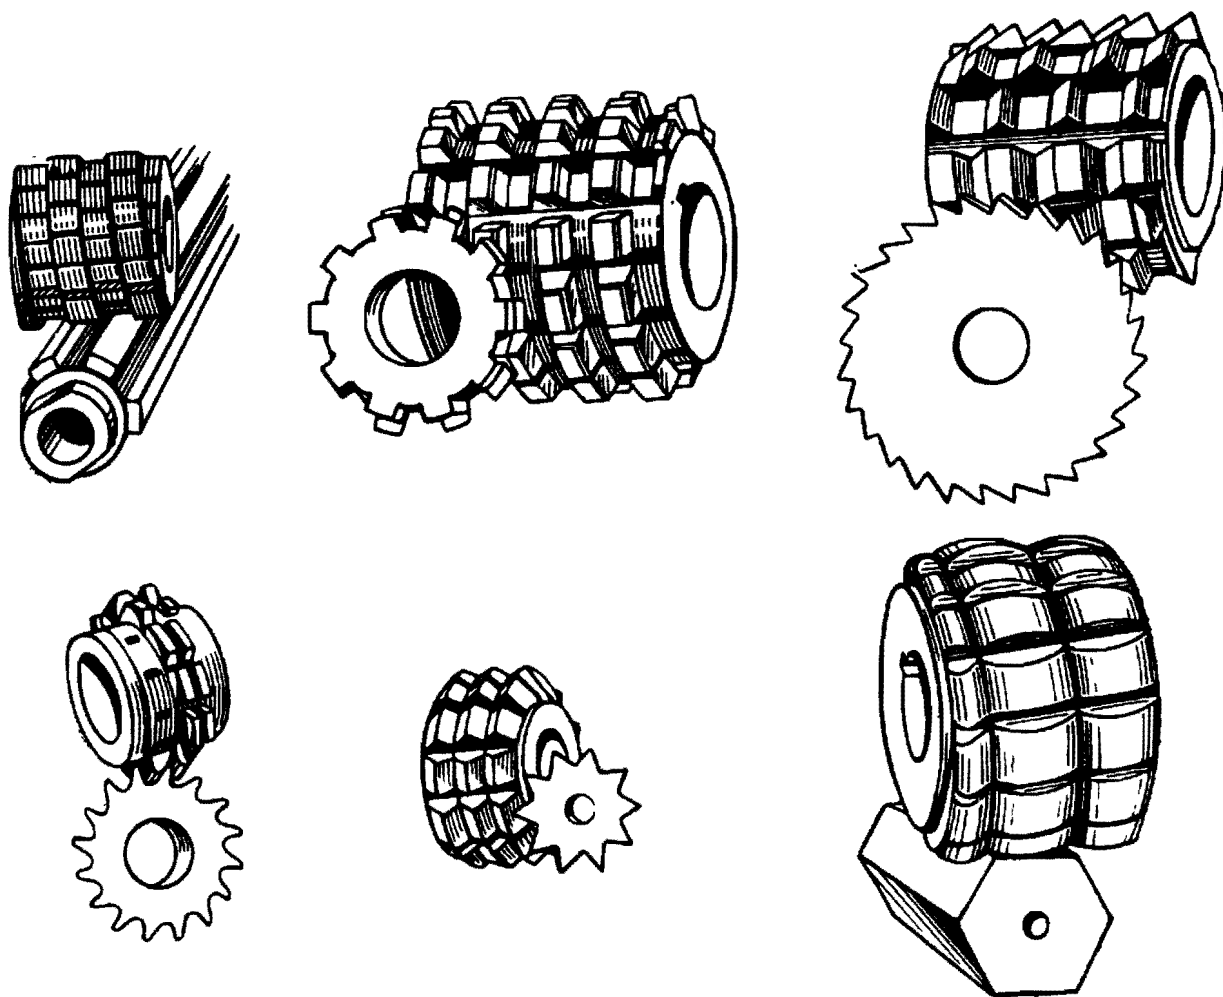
Примеры фрезерования червячными фрезами различных деталей
